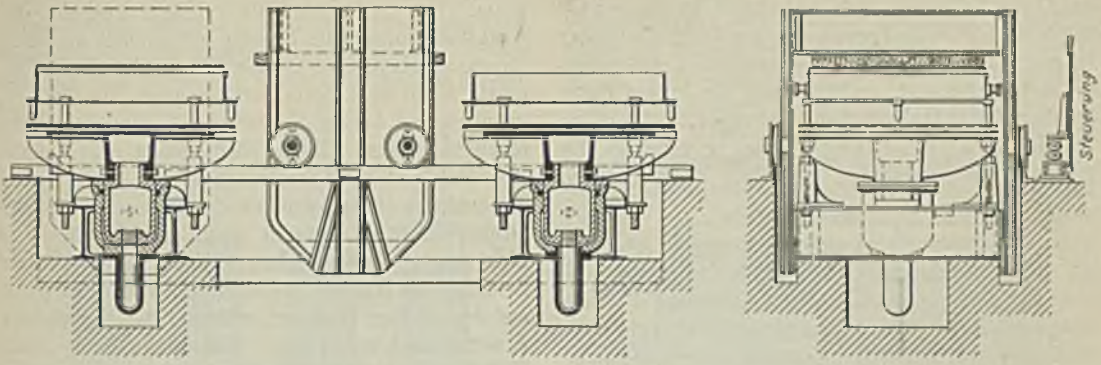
Doppelte Maschine für einfache Pressung mit gemeinschaftlichem fahrbarem Preßholm.
